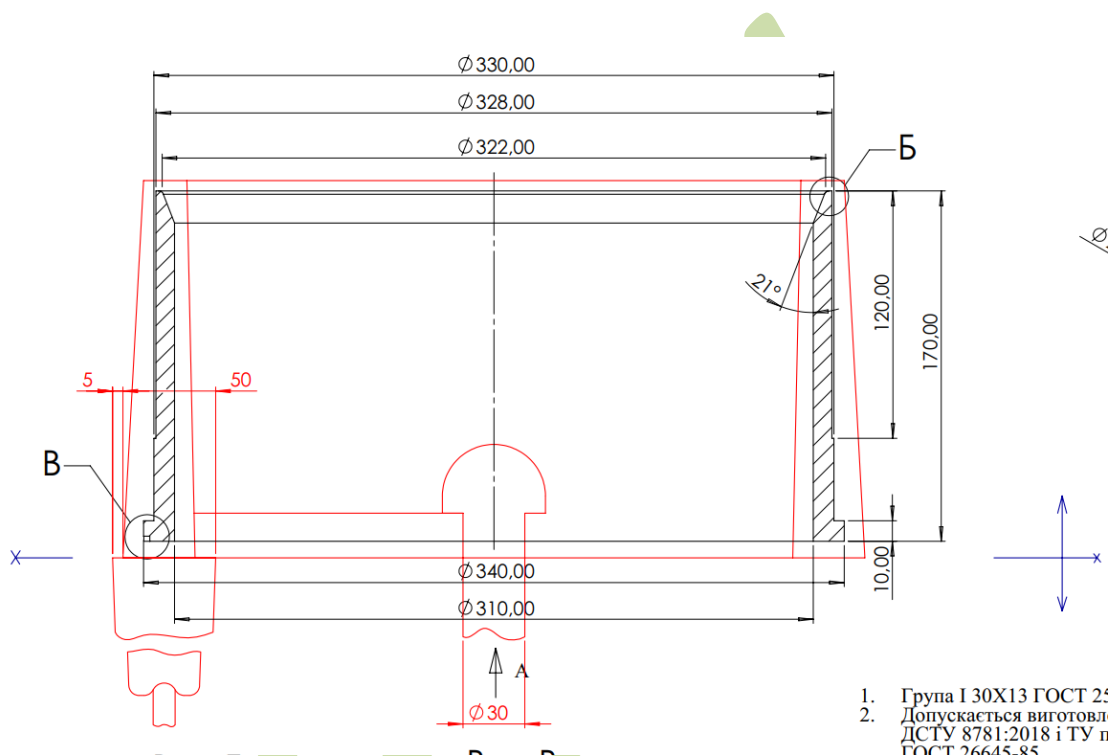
Ливарний варіант креслення деталі «штулка»
